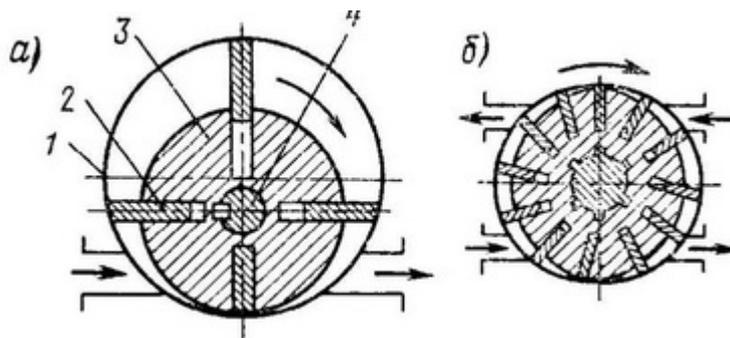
Пластинчатый насос: а — простого действия; б — двойного действия.
